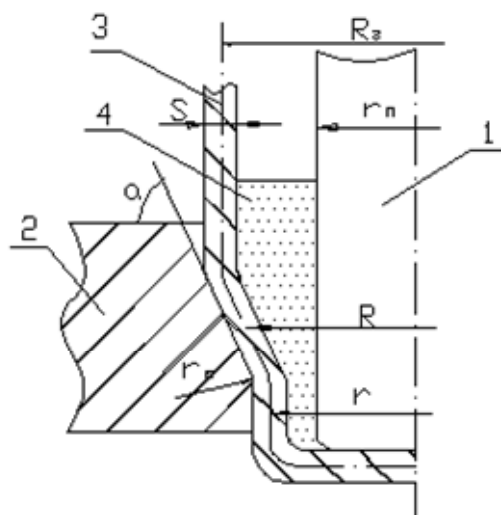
Схема вытяжки втулки подшипника: 1 – пуансон; 2 – матрица; 3 – стальная поллая заготовка; 4 – порошок оловянистой бронзы
